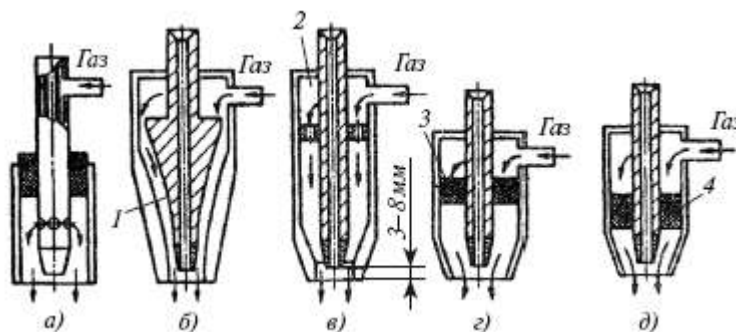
Схемы питания сварочных горелок защитным газом: а – с кольцевым подводом газа; б – с отражателями (1); в – с успокоительными камерами (2); г – с сеточными вставками (3); д – с металлокерамическими вставками (4)
